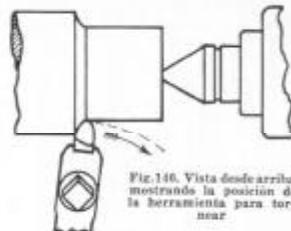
Vista desde arriba mostrando la posición de la herramienta para torneado
